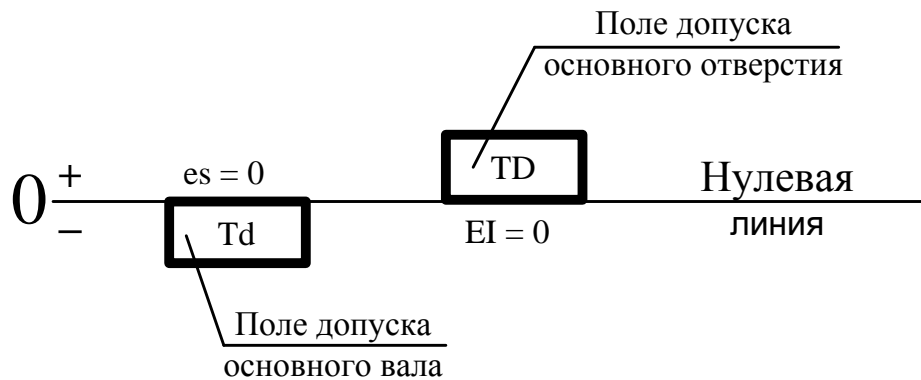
Поля допусков основного вала и основного отверстия
